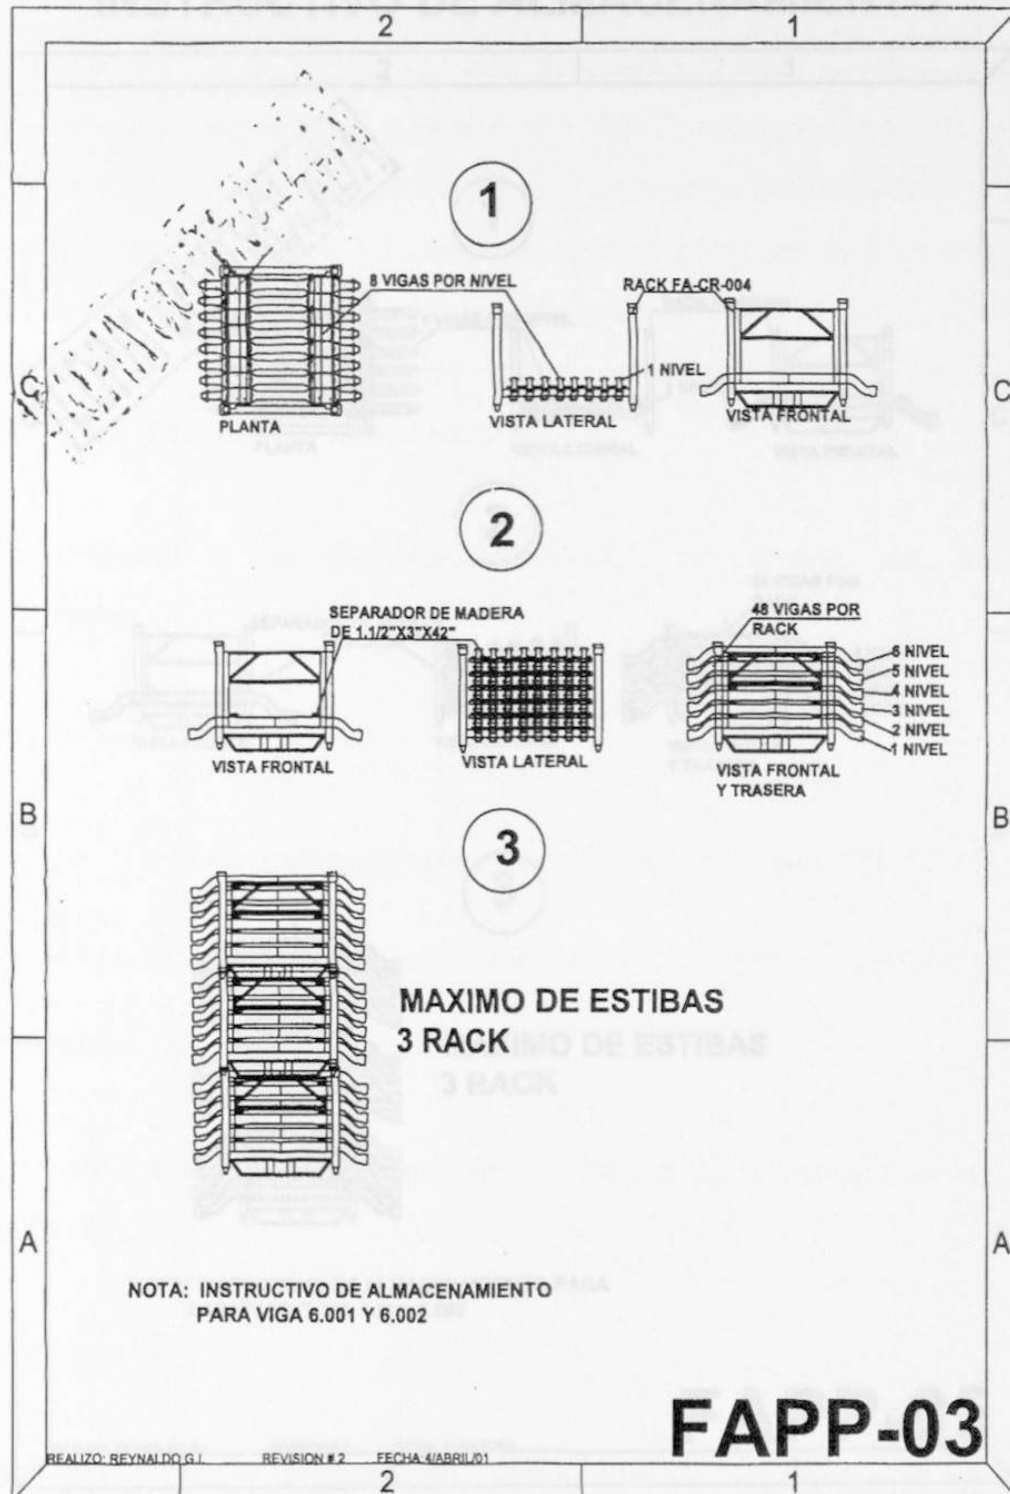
Instructivo para almacenamiento de viga 6.001 y 6.002.
